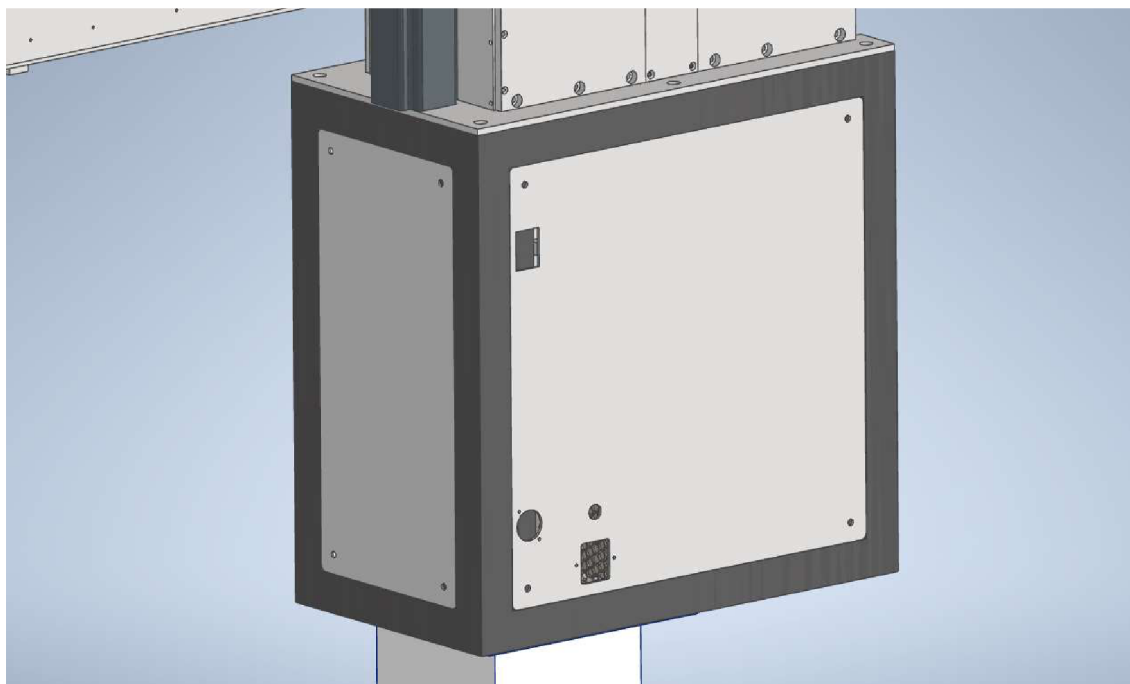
Přední pohled na spodní pojízdnou konstrukci
